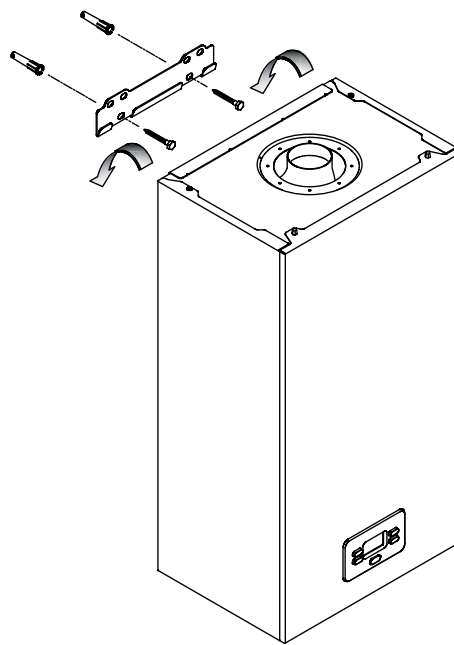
Instalación de Aquwa 12 en la placa colgante de montaje
